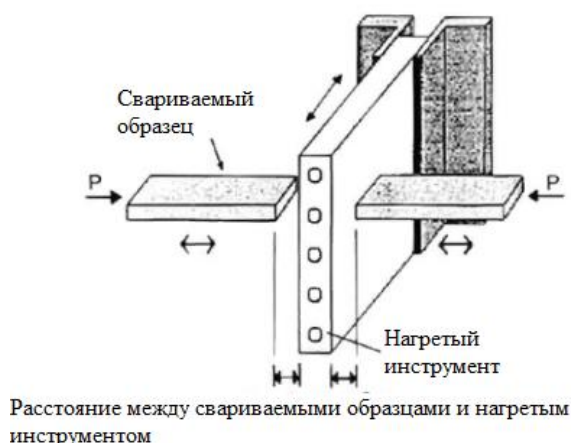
бесконтактная сварка нагретым инструментом.
